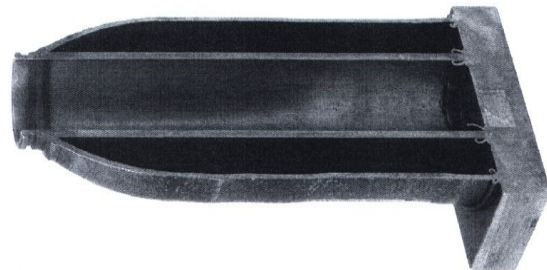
Partie d'un cric hydraulique: le tube à double paroi est soudé en une fois [1].
